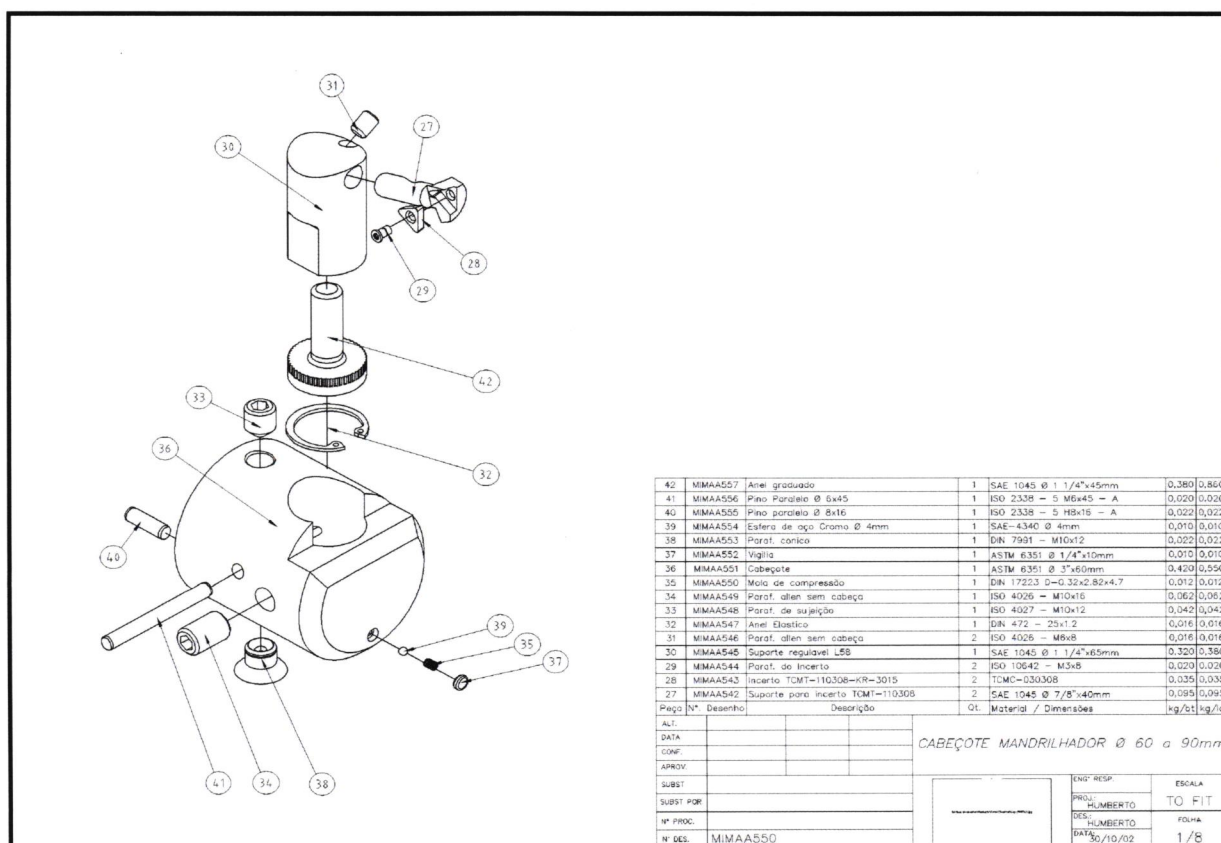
Desenho da vista explodida do cabeçote mandrilador
